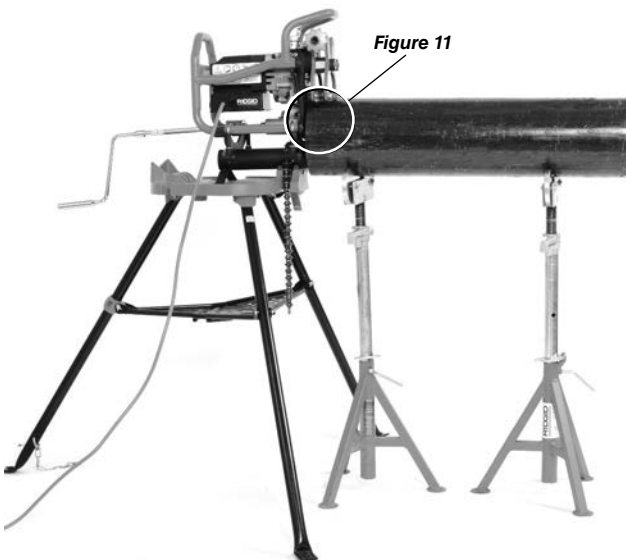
Machine fixe, tuyau de grande longueur, porte-tubes multiples
